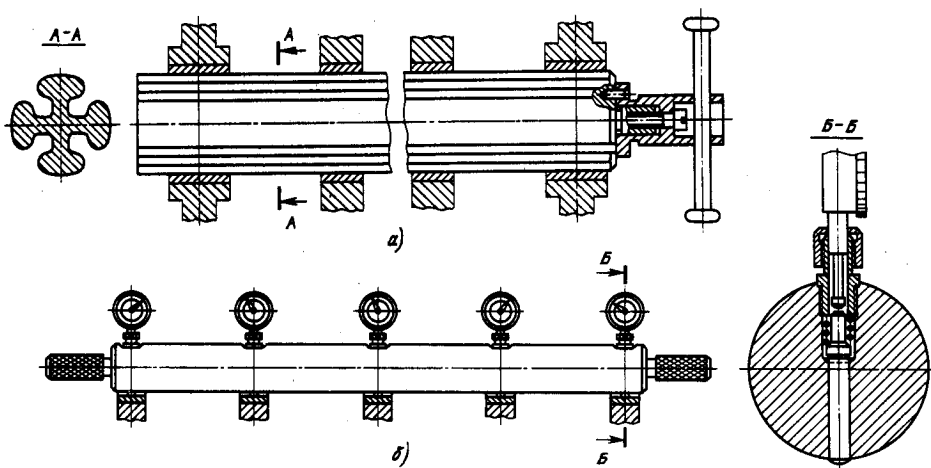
Проверка соосности втулок многоопорного вала: а — контрольной скалкой; б — скалкой с индикаторами
